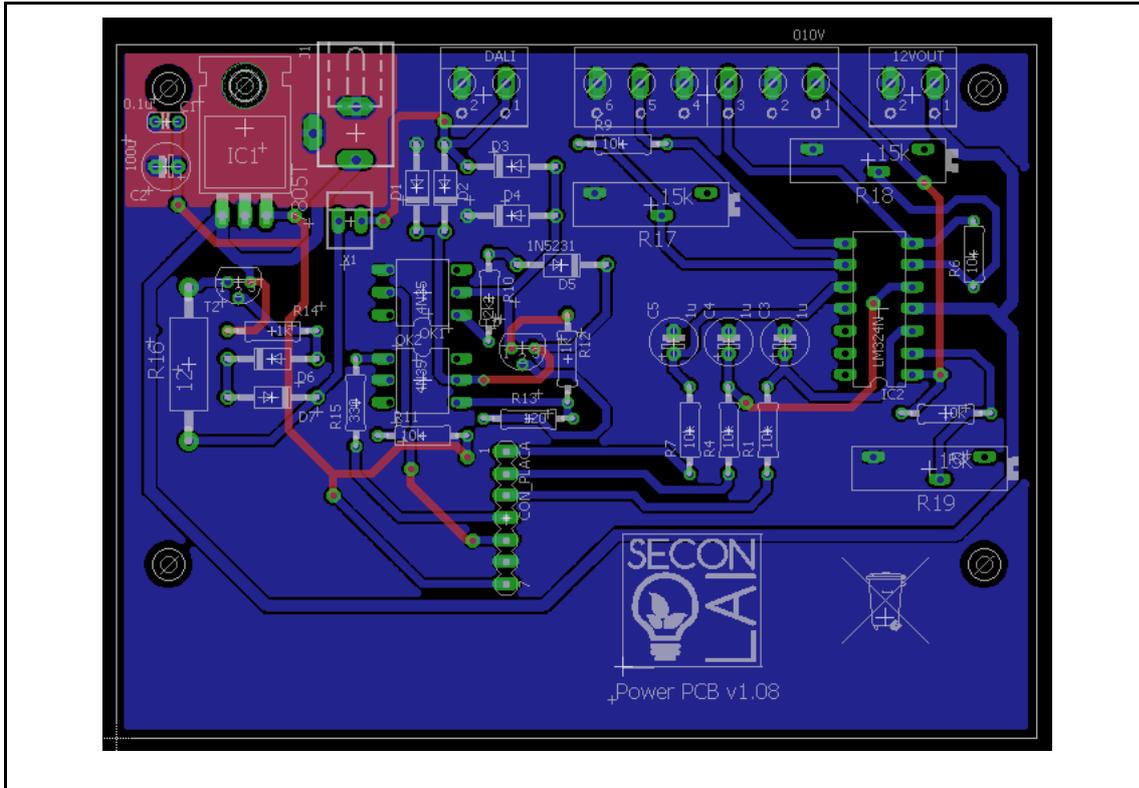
DISEÑO Y RUTEO DE PCB DE POTENCIA
